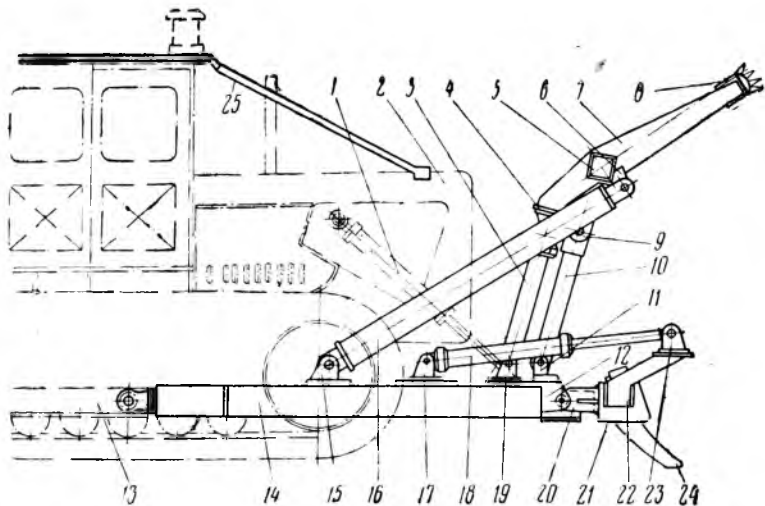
Устройство древовала-корчевателя «Вебрь»:
